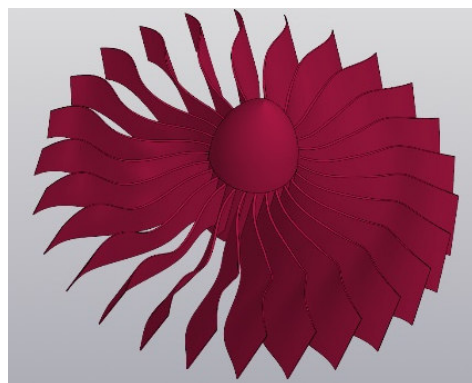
3D-модель компрессора низкого давления турбореактивного двигателя
